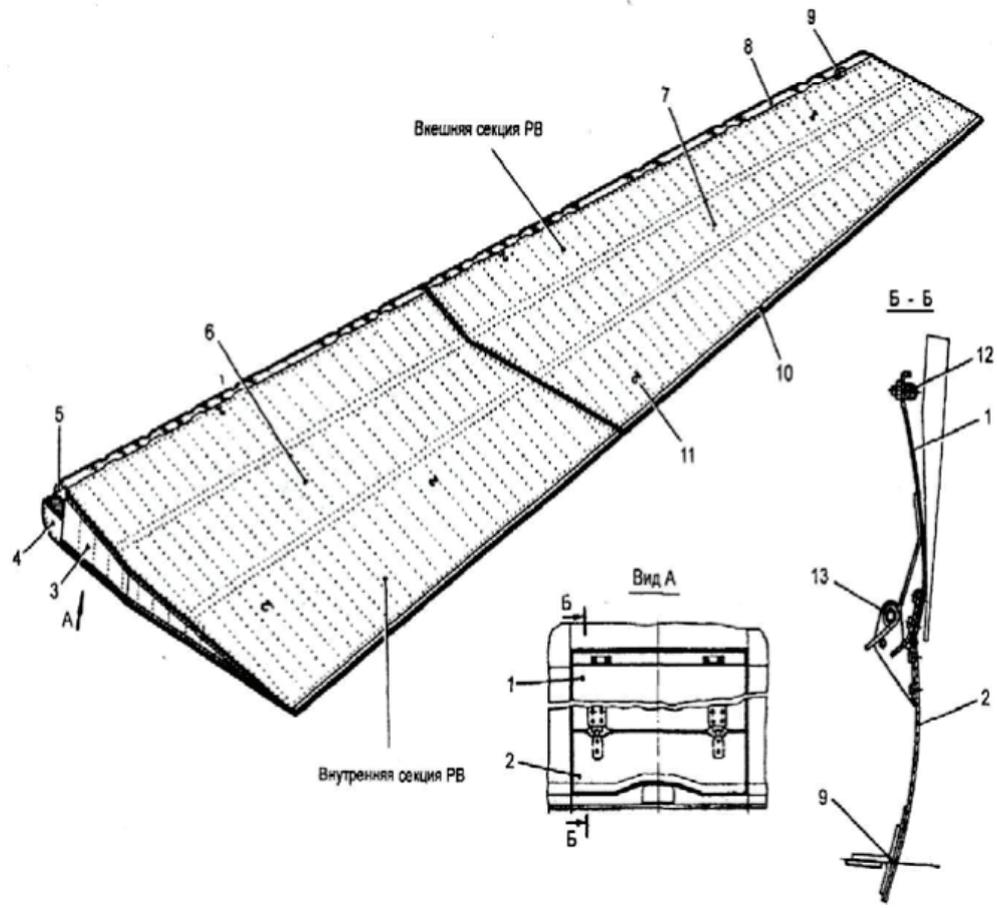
Руль Высоты самолета АН-124. [1, стр. 14]. 1 — створка; 2 — крышка; 3 — торцевая нервюра; 4,5 — диафрагмы носка; 6,7 — верхние панели; 8 — носок; 9 — лонжерон; 10 — законцовка; 11 — такелажный узел; 12 — фторопластовый упор; 13 — пружина
